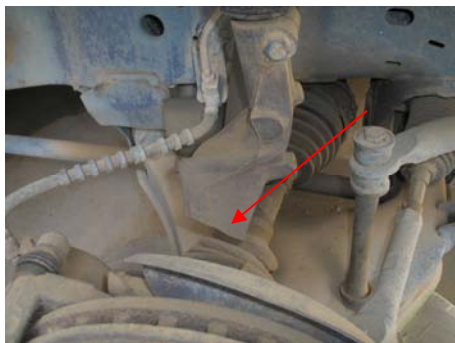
Ponta de eixo fraturada, conjunto montado.
